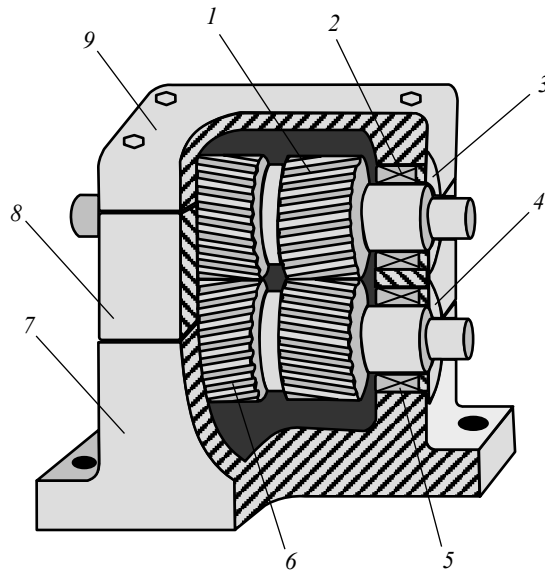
Шестеренна кліть: 1, 6 — шестеренні валки; 2, 5 — підшипники; 3, 4 — кришки підшипників; 7, 8 — складений корпус; 9 — кришка
